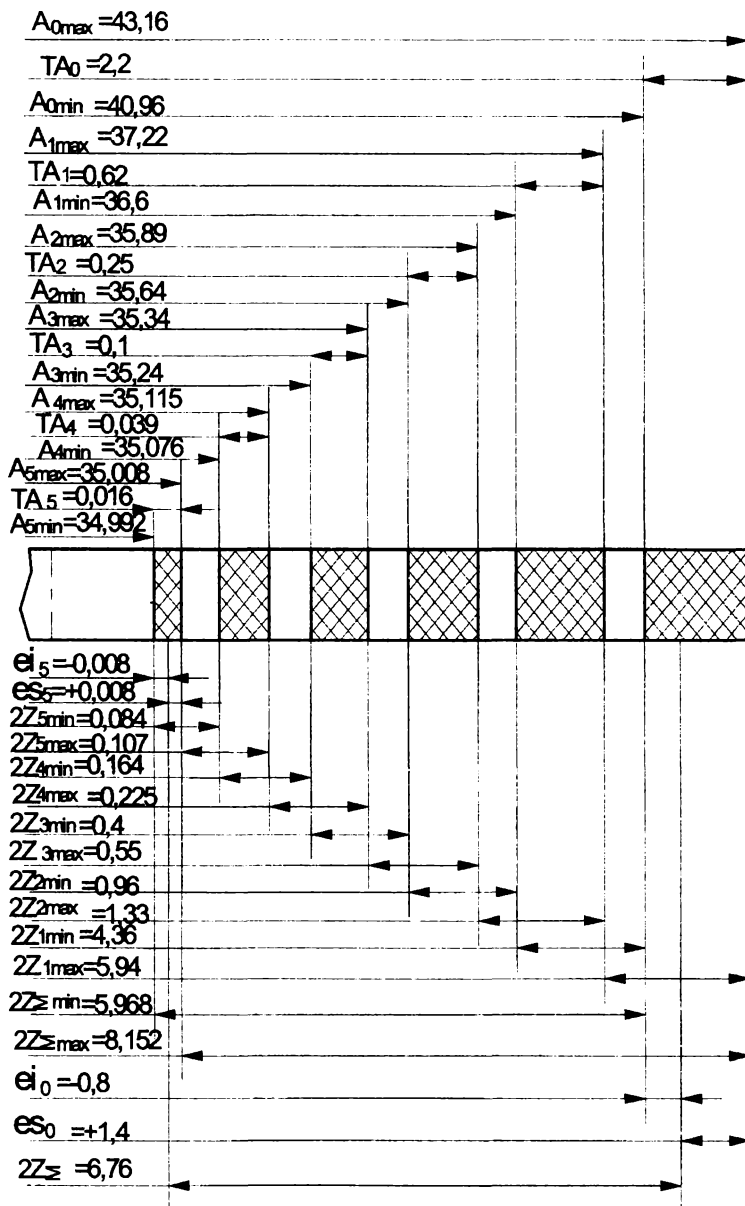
Схема расположения припусков, допусков и предельных размеров для шейки вала диаметром 35 $\pm$ 0,008
